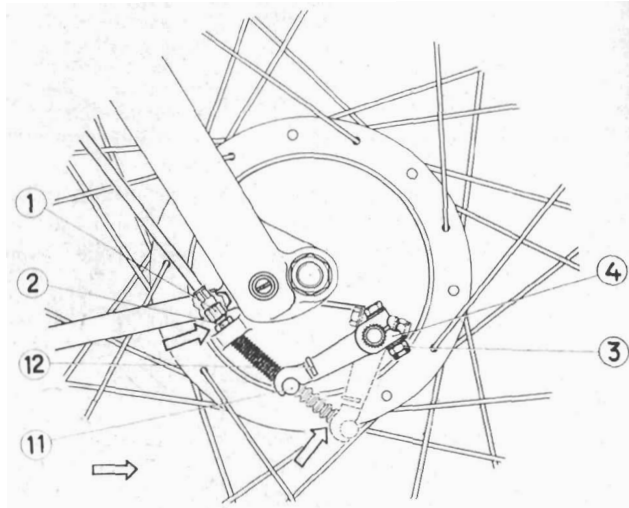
Freno delantero: Reglaje, recuperación desgaste y engrase.
